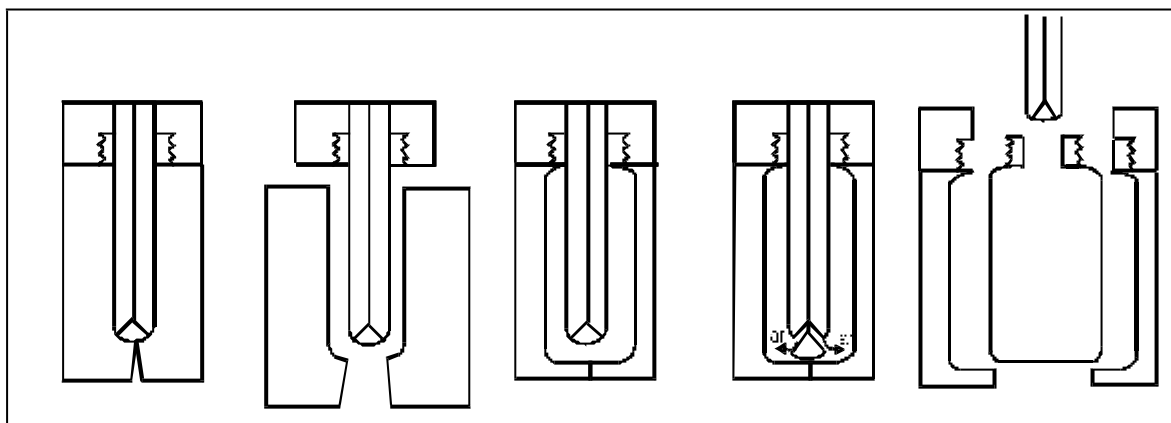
Processo de injeção-sopro do PET. (a) injeção da pré-forma; (b) desmoldagem da pré-forma; (c) substituição dos moldes; (d) sopro; (e) desmoldagem da garrafa. (CHARRIER, 1990).
